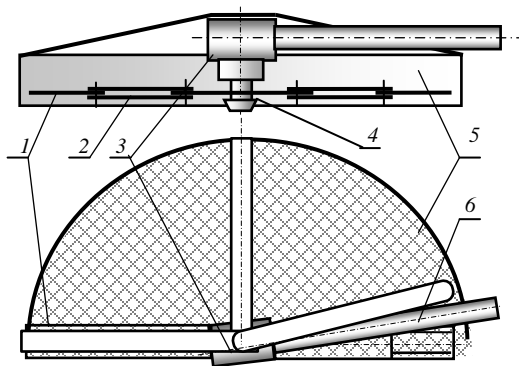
Схема однороторной двухножевой косилки: 1 – ножи; 2 – серги; 3 – редуктор; 4 – траверса; 5 – кожух; 6 – стрела
